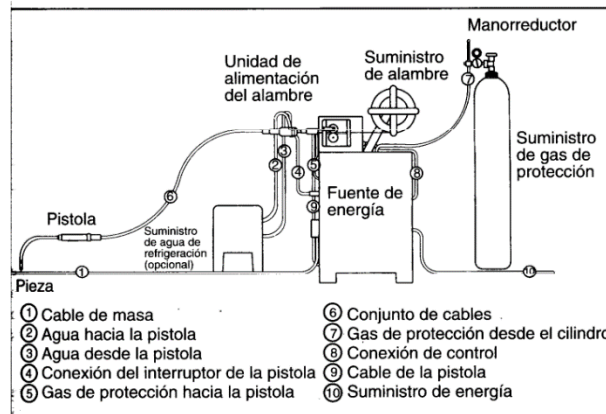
Equip de soldadura MIG/MAG. Apunts Tecnologia Mecànica.
